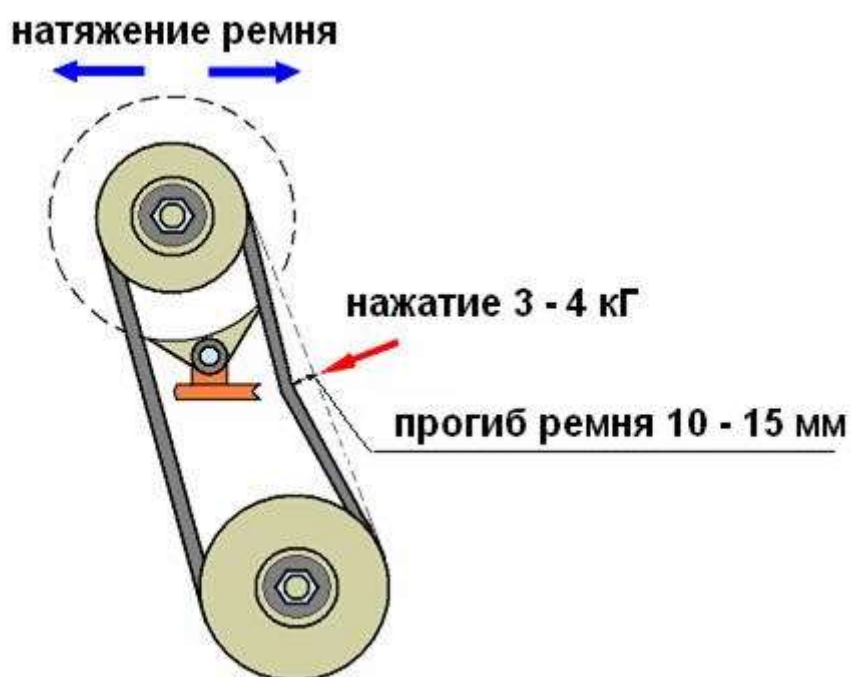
Проверка и регулировка натяжения приводного ремня генератора
